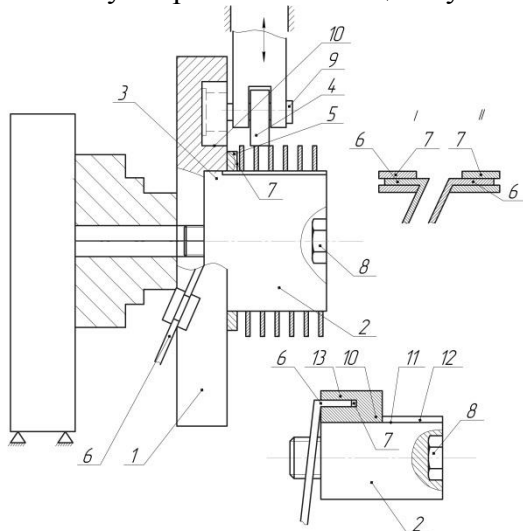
Універсальний пристрій для виготовлення гвинтових заготовок
